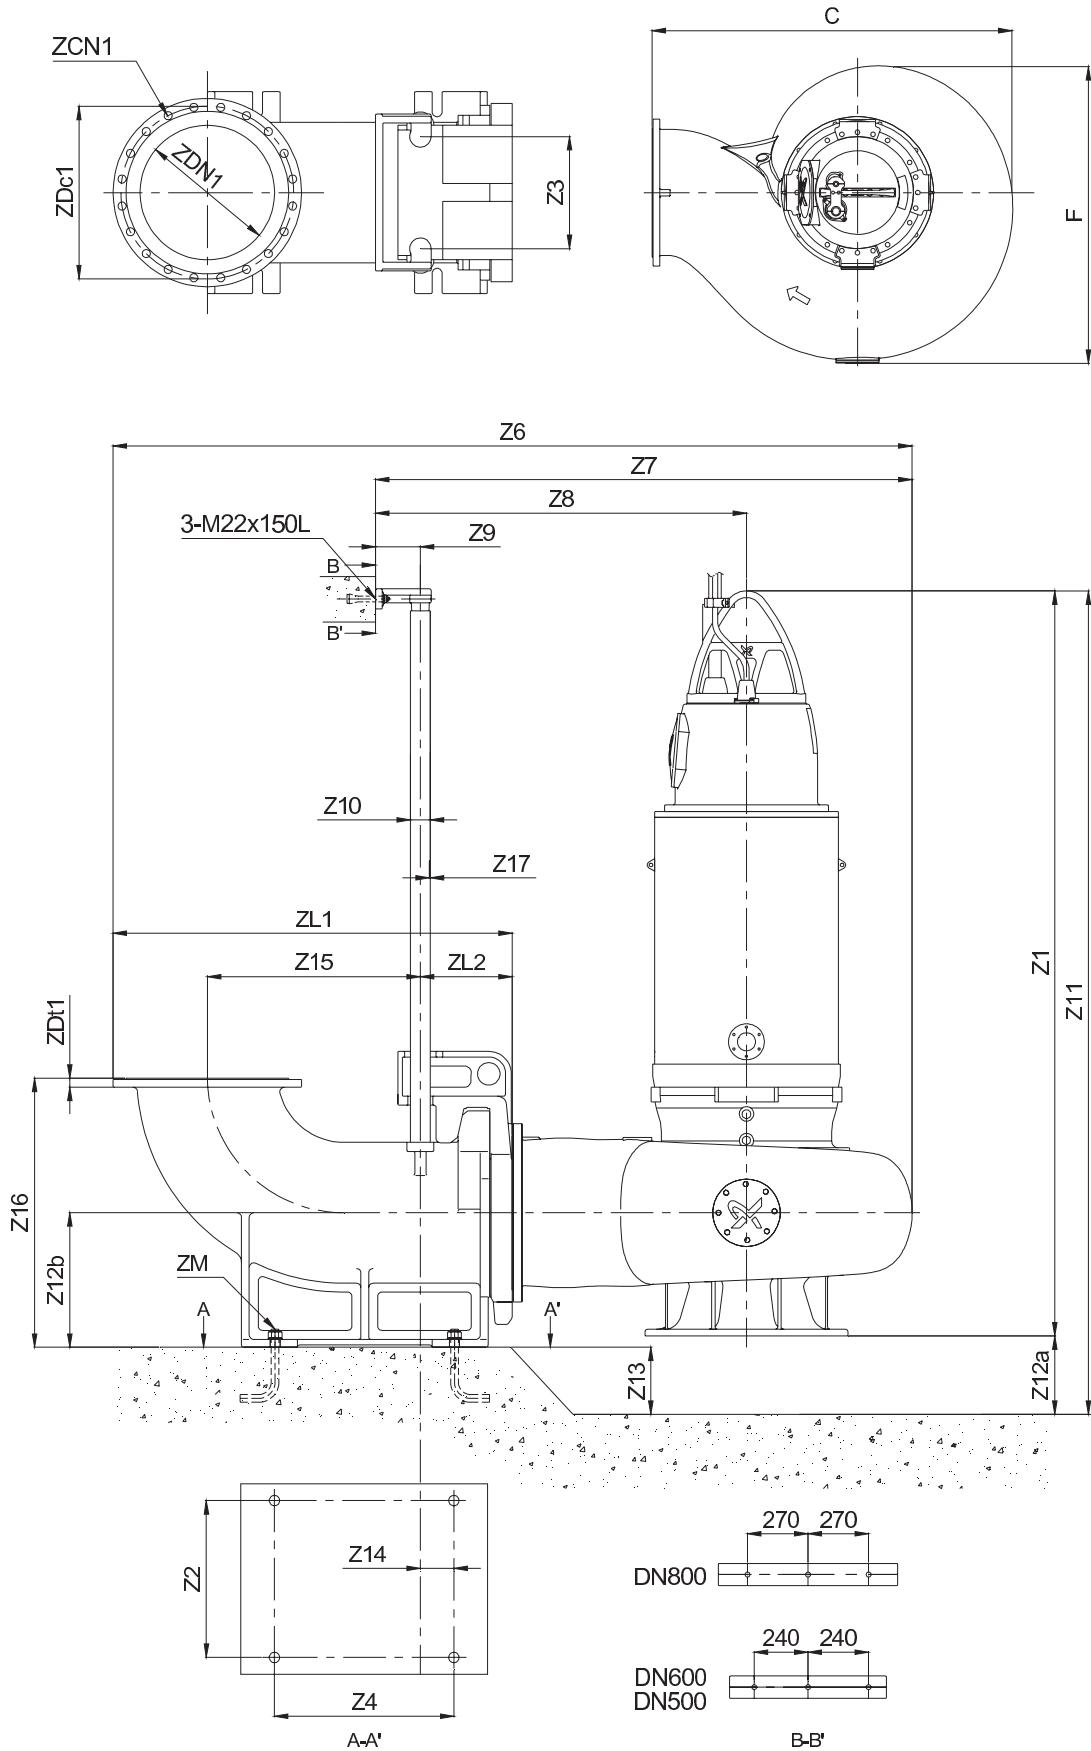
Габаритные чертежи, установка на автоматической трубной муфте
